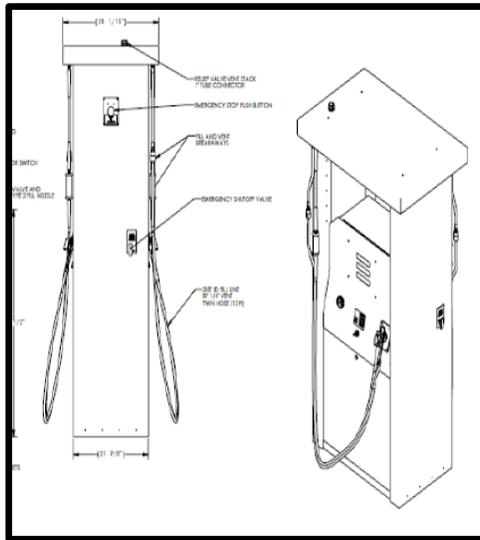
Maquina que dispensa GNC en las islas.
